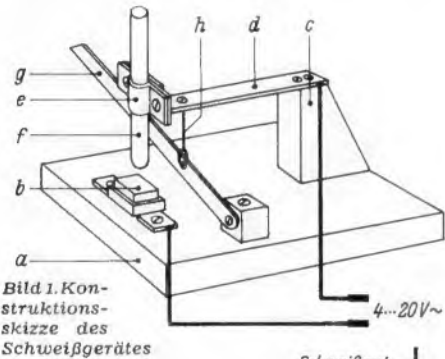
Konstruktions-skizze des Schweißgerätes
